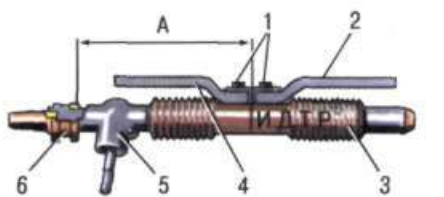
Нейтральное положение рейки, соответствующее прямолинейному движению автомобиля: 1 – болты крепления рулевых тяг; 2 – правая рулевая тяга; 3 – кожух картера рулевого механизма; 4 – левая рулевая тяга; 5 – картер рулевого механизма; 6 – левая опора
